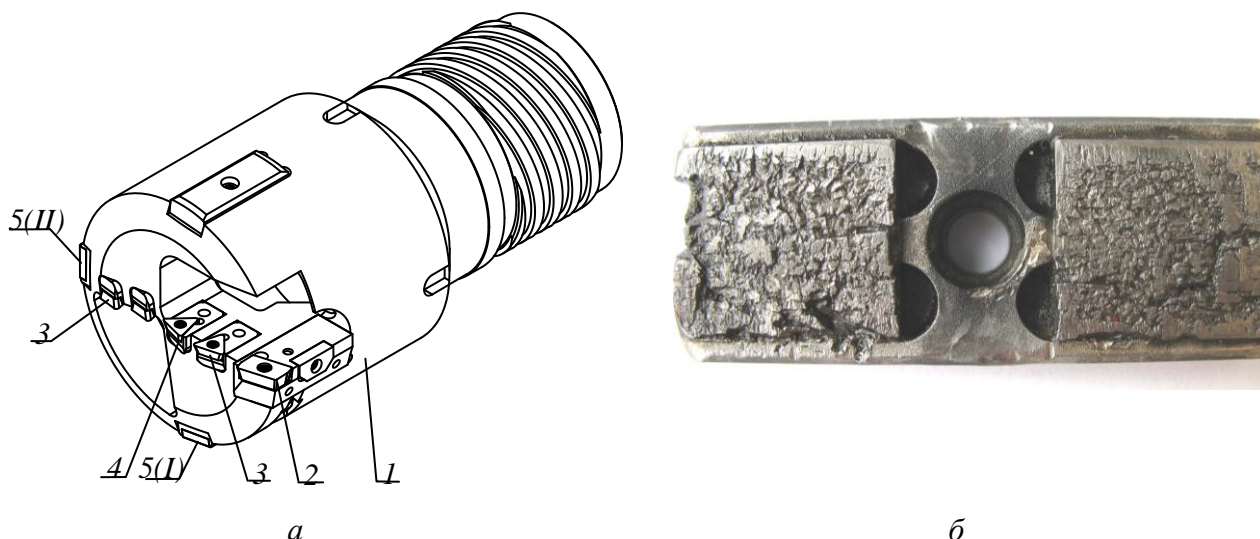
Головка глубокого сверления (а); фото направляющей опоры с катастрофически изношенной поверхностью
